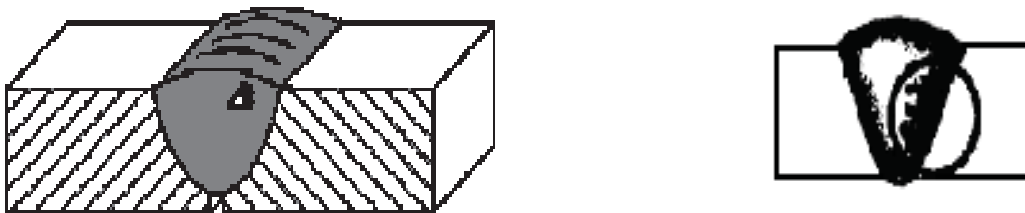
Схематичное изображение шлакового включения сварного соединения
